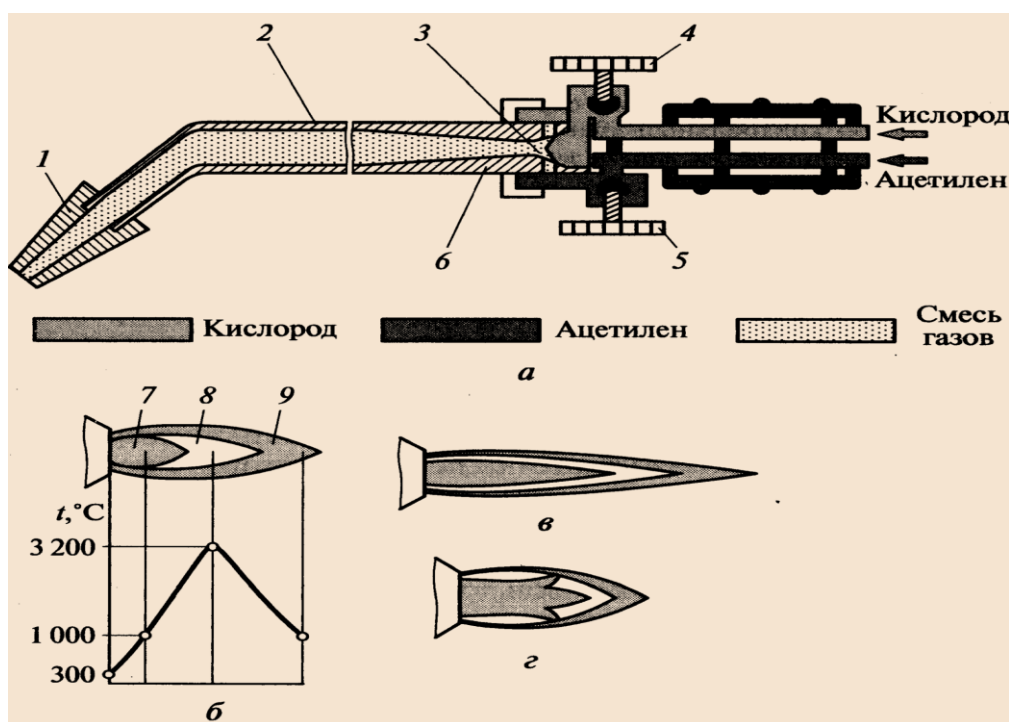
Схема газосварочной горелки инжекторного типа (а) и виды (б – г) ацетилено-кислородного сварочного пламени:
